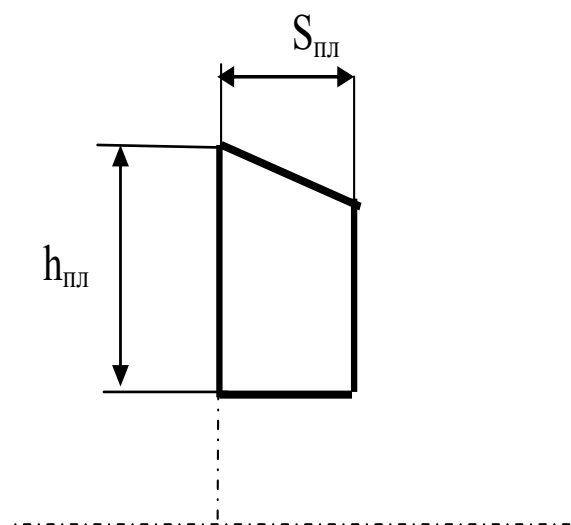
Схема установки пластин в корпуса концевых фрез по ГОСТ 20536-75–ГОСТ20538-75
